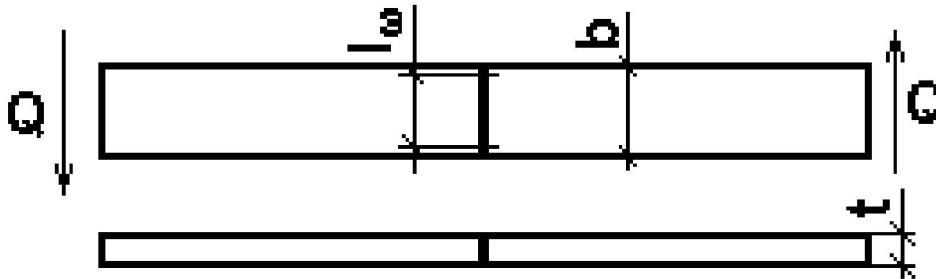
К расчету стыкового сварного шва
